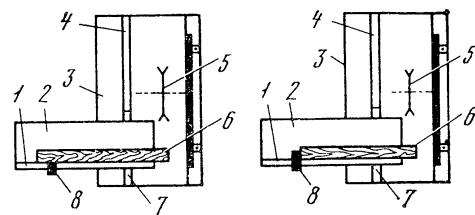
Схема торцевания на однопильном торцовочном станке с кареткой:
